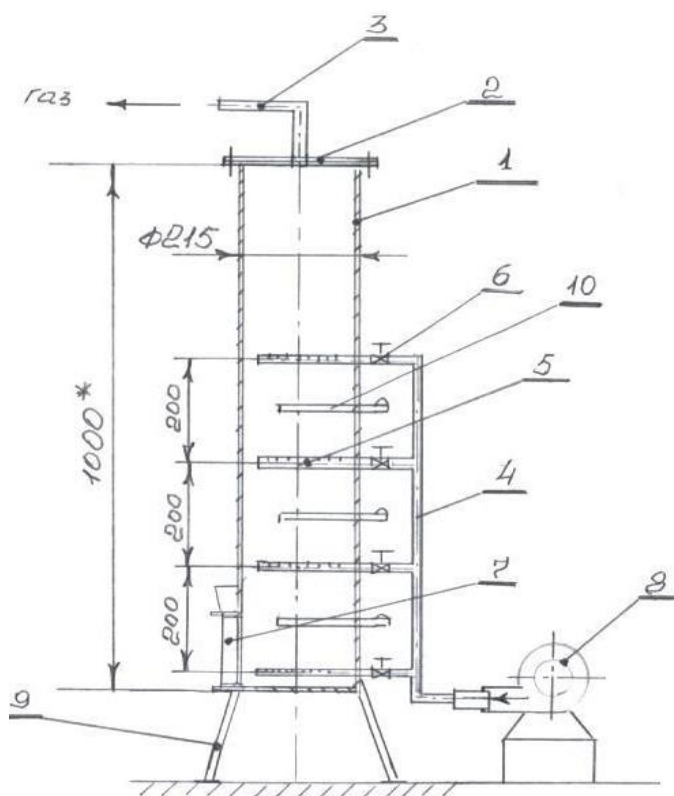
Принципиальная схема пиролизной установки по переработке угольной мелочи: 1– корпус цилиндра, 2–загрузочное устройство с крышкой, 3–патрубок для отвода газа, 4– общий воздухопровод, 5–воздуховод с прорезями, 6–кран воздушный, 7–песочный затвор, 8– вентилятор, 9–стойки, 10–термодатчик.
